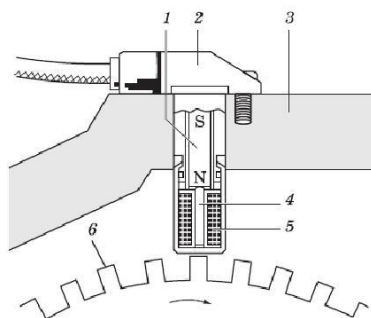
Индуктивный датчик в корпусе редуктора
